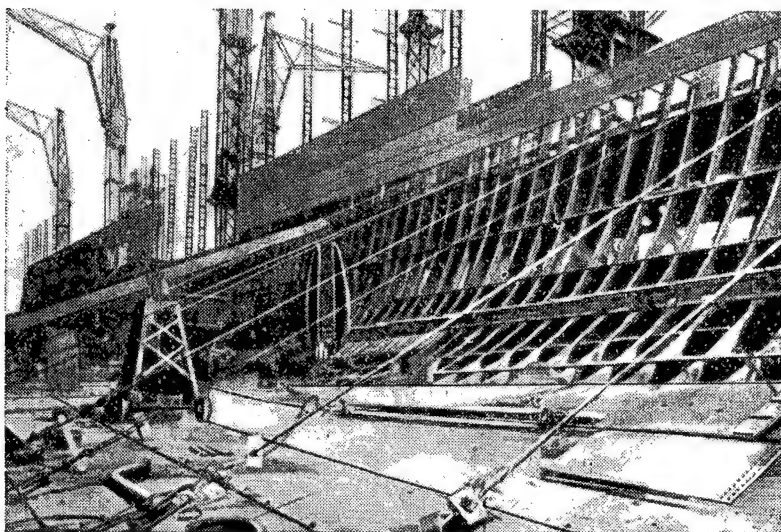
Сборка настила второго дна и установка бортового набора на клепаное судно
